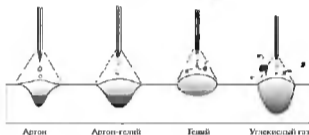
Форма сварного шва и глубина проплавления для различных защитных газов
